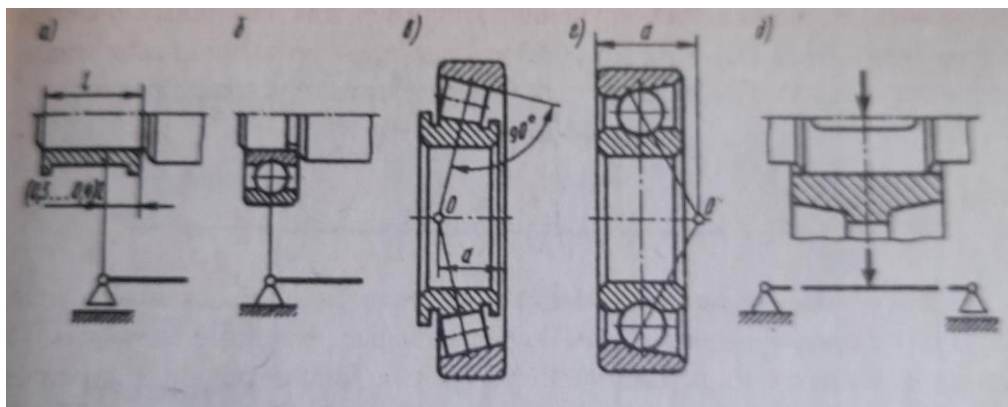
Расчетные схемы подшипниковых опор
